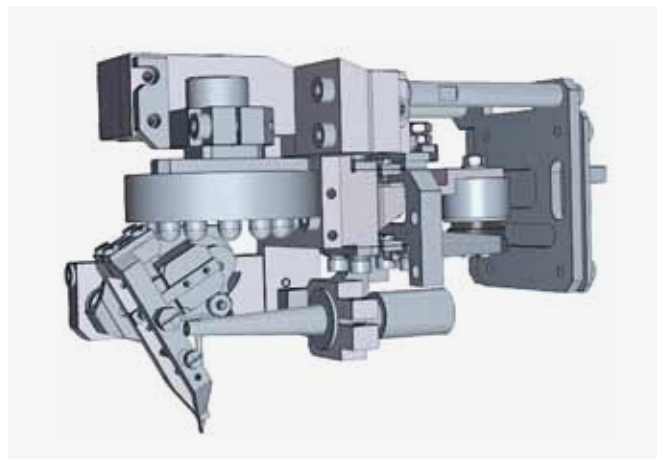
Сварочная головка установки ЭМ-4520
